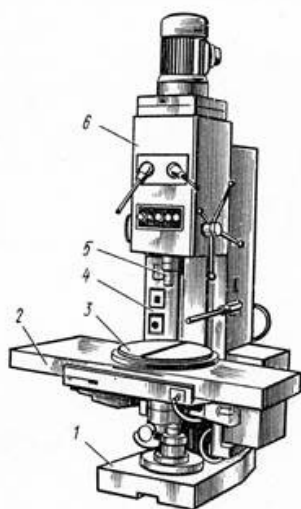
Внешний вид станка мод. 2Н135-1:
